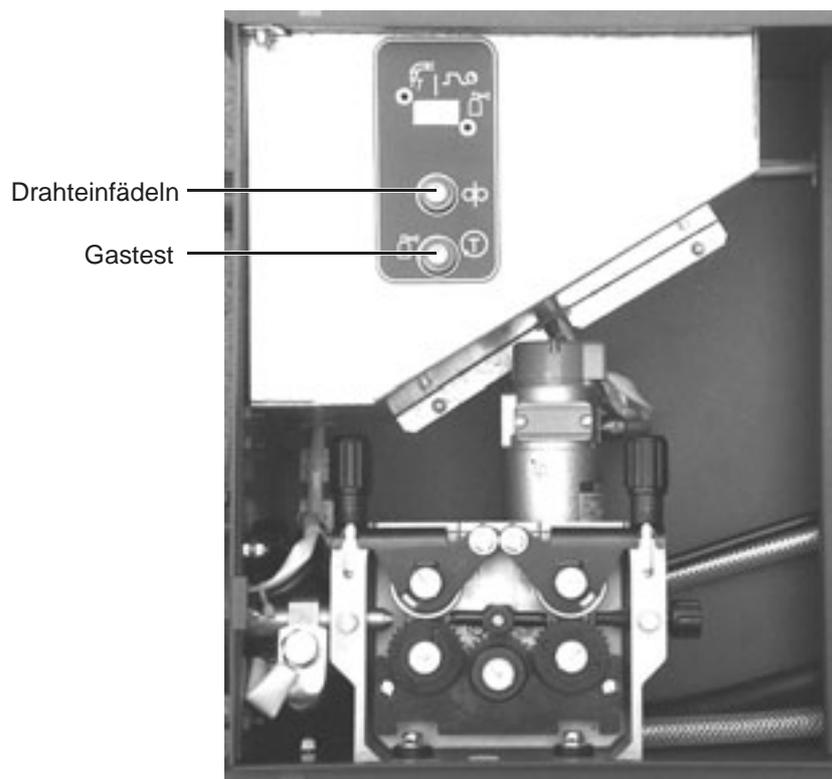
Кнопки для проверки газа и заправки сварочной проволоки в переносном узле подачи проволоки
